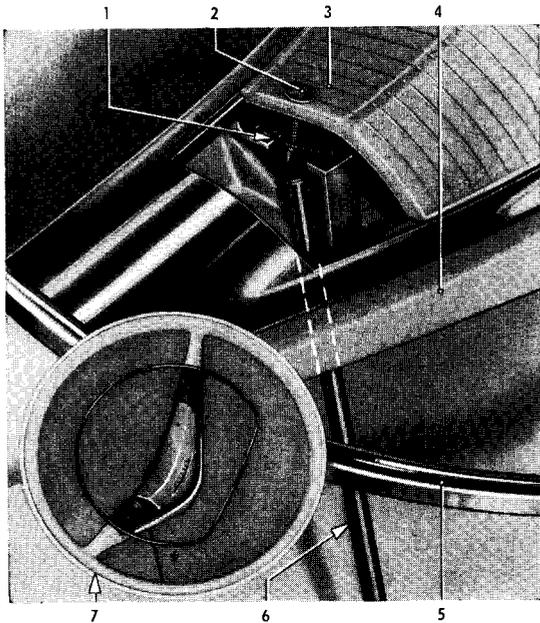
Gewindestifte für Zierstückbefestigung herausdrücken
